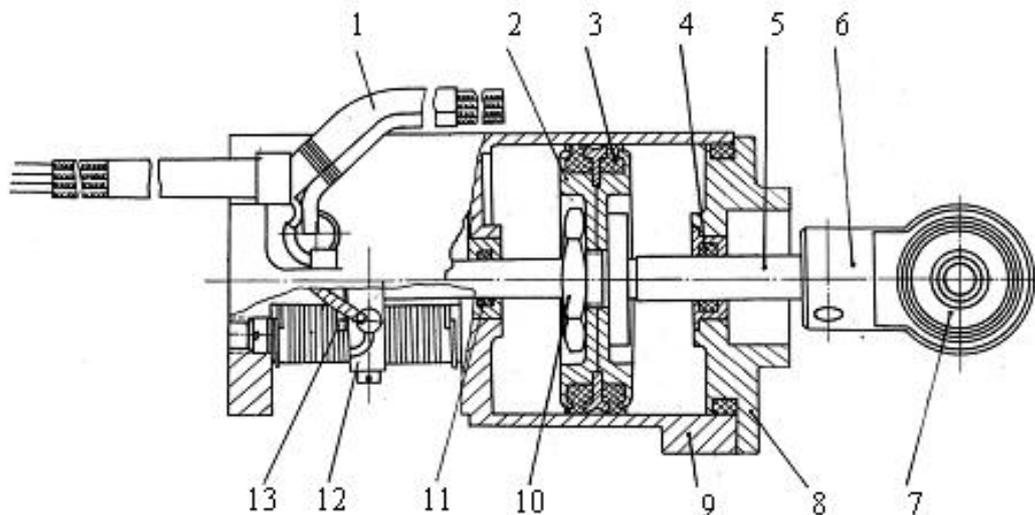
Рулевая машина: 1 – электрожгут; 2 – диск; 3 – резиновая манжета; 4,11 – уплотнительные кольца; 5 – шток; 6 – серьга; 7 – подшипник; 8 – крышка; 9 – корпус; 10 – гайка; 12 – потенциометр обратной связи; 13 – контактная пластина; 14 – движок потенциометра
